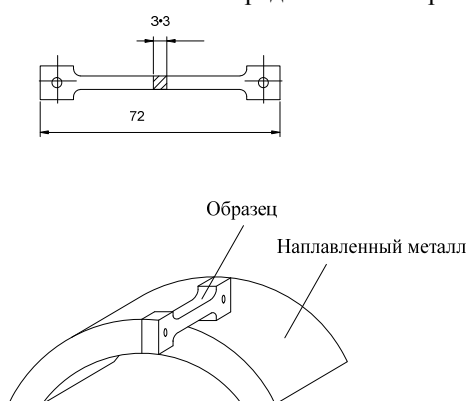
Общий вид образца для высокотемпературных исследований и схема его вырезки из наплавленного металла
